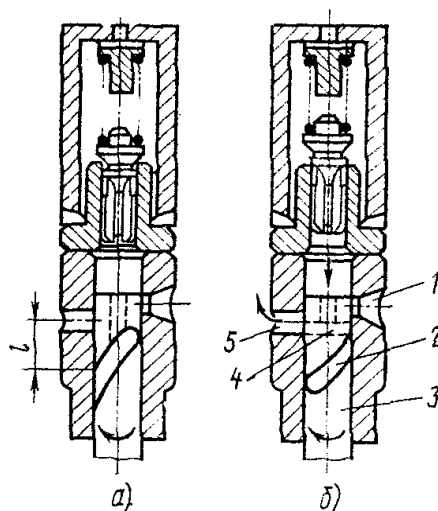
Схема регулювання подачі палива поворотом плунжера:
